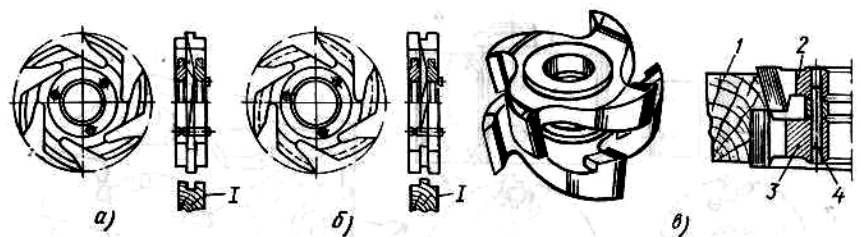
Составные фрезы к четырехстороннему продольно-фрезерному станку для обработки:
